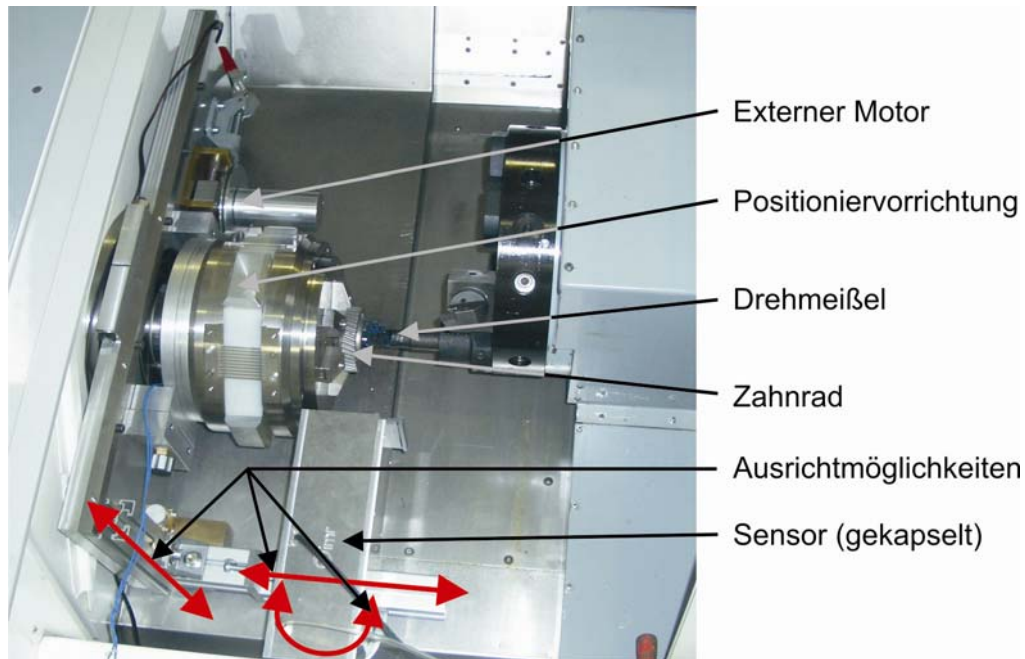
Integration der Sensorik in die Werkzeugmaschine (Zahnrad) [4]
